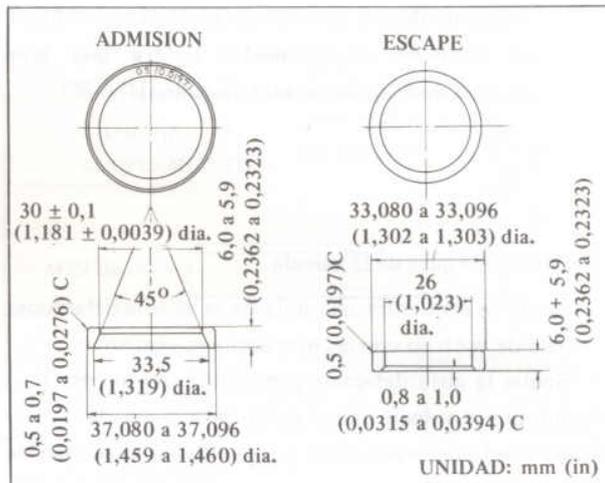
Inserción del asiento de la válvula standard (Motor A10 y A12)
